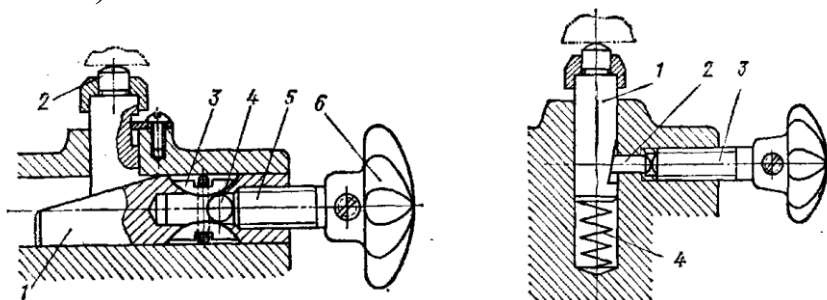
Подводимая опора и самоустанавливающаяся опора
